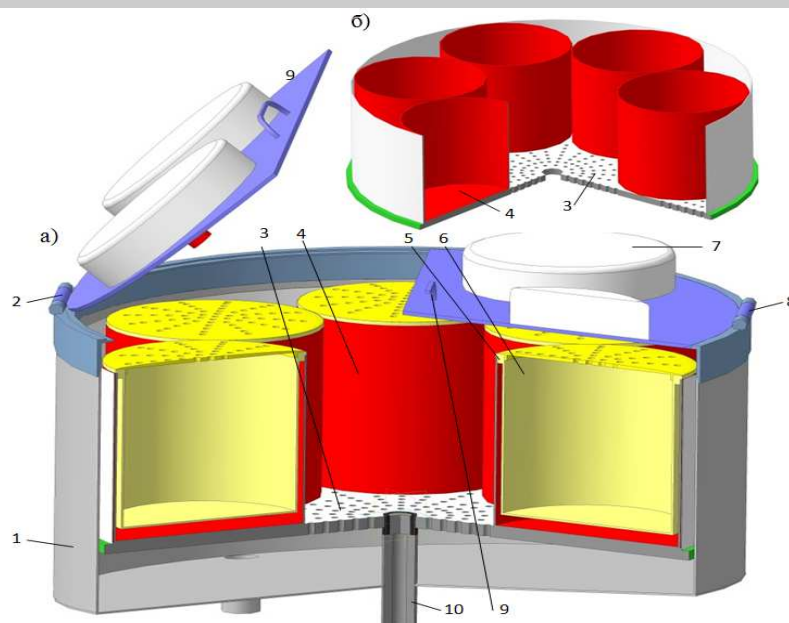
Сверхвысокочастотная установка для варки отходов убоя птицы и животных: а) – вид общий; б) – расположение резонаторов на диск-роторе; 1 – экранирующий корпус; 2 – открывающаяся крышка экранирующего корпуса; 3 – перфорированный диск-ротор; 4 – цилиндрические резонаторные камеры с перфорированными основаниями; 5 – цилиндрические диэлектрические контейнеры с перфорированными крышками и силиконовым покрытием; 6 – фиксаторы контейнеров; 7 – сверхвысокочастотные генераторные блоки; 8 – шарнирные петли; 9 – ручки на крышке корпуса; 10 – вал, закрепленный на опорный диск
